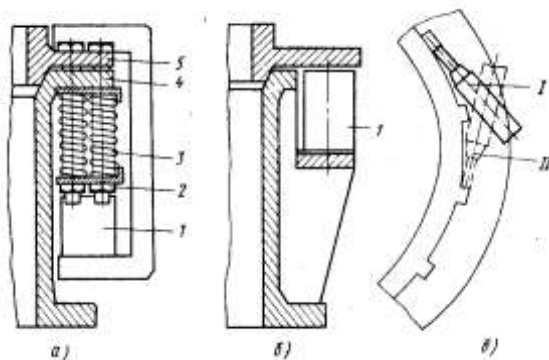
Схема приспособлений для механизации трудоемких операций: а – установка гидродомкрата для регулирования затяжки амортизирующих пружин; б – установка гидродомкрата для распрессовки камеры дробления; в – устройство для поворота регулирующего кольца.
